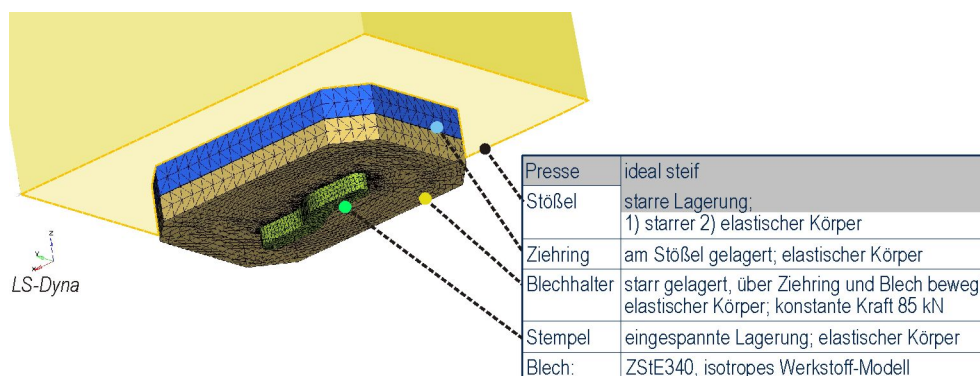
Elastische Werkzeugbeschreibung mittels FEM für das Bauteil „S-Rail“
